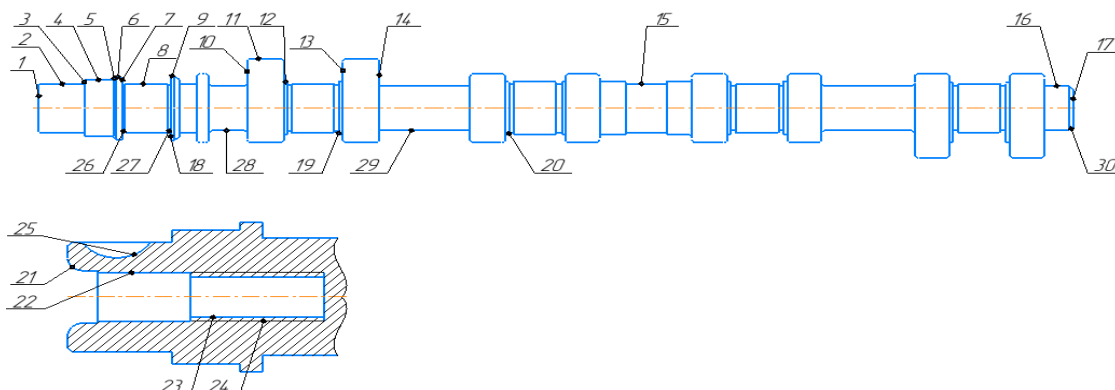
Общий вид чертежа распределительного вала в двигателе «ВАЗ - 21126»
